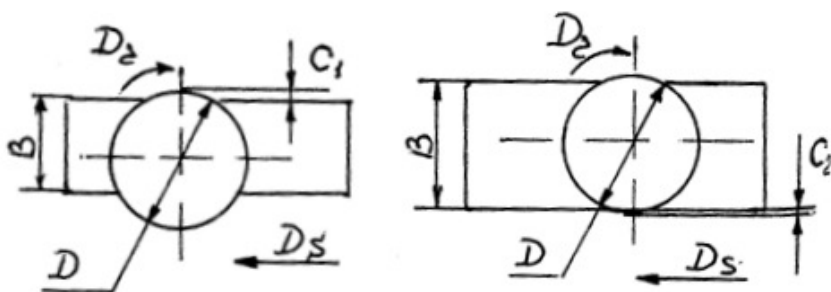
Несиметричне розміщення сталевих заготовок відносно фрези
